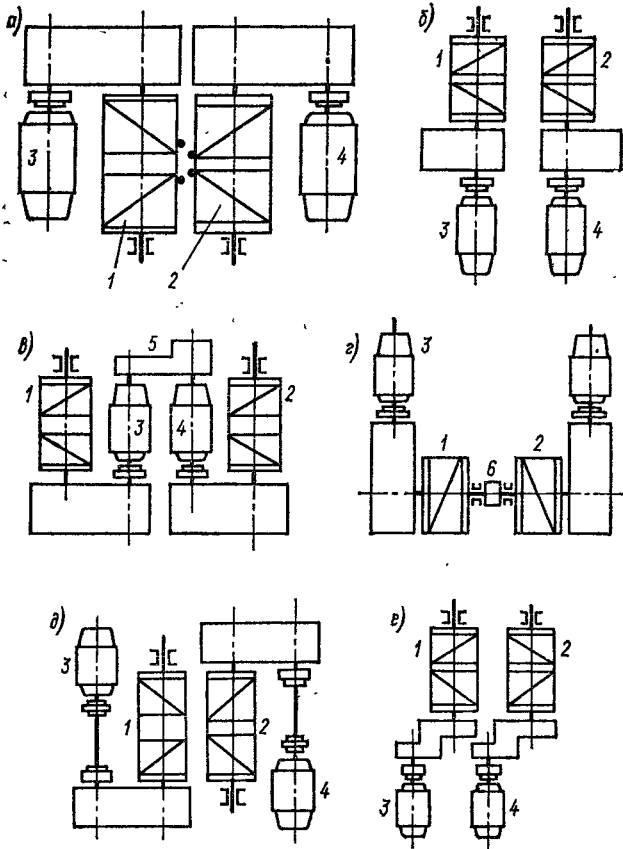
Схемы грейферных двухмоторных лебедок с независимыми барабанами: а, д — нормальное расположение; б — соосное расположение двигателей и барабанов; в — с редуктором-синхронизатором б; г — с кулачковой муфтой б для жесткой связи барабанов; е — расположение при стесненных габаритах (см. рис. IV.4.2)
